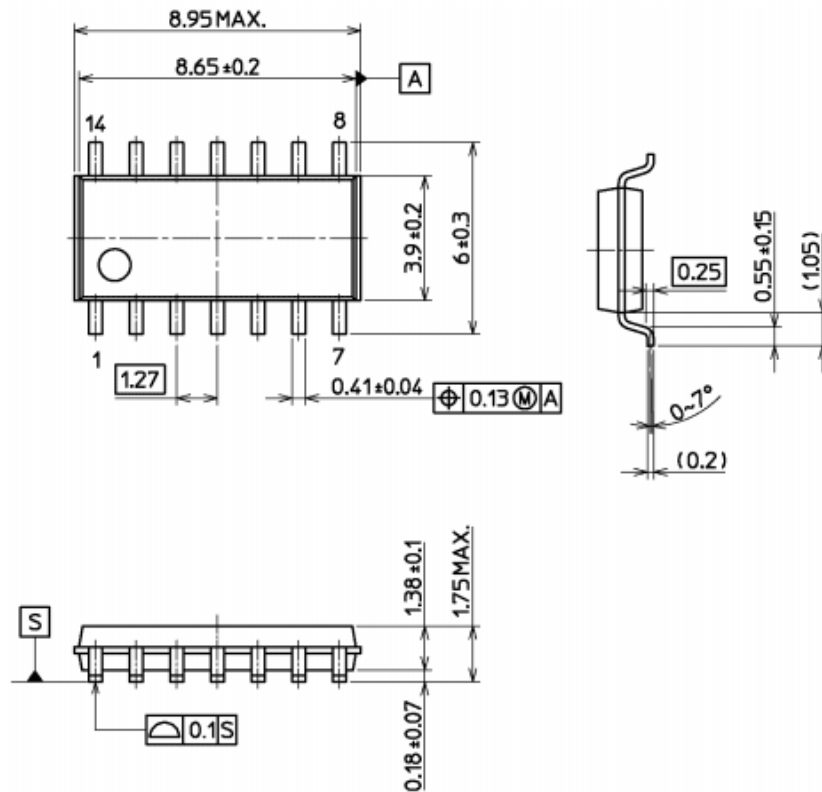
Зовнішній вигляд та габаритні розміри операційного підсилювача LM324ADT в корпусі SOIC-14
